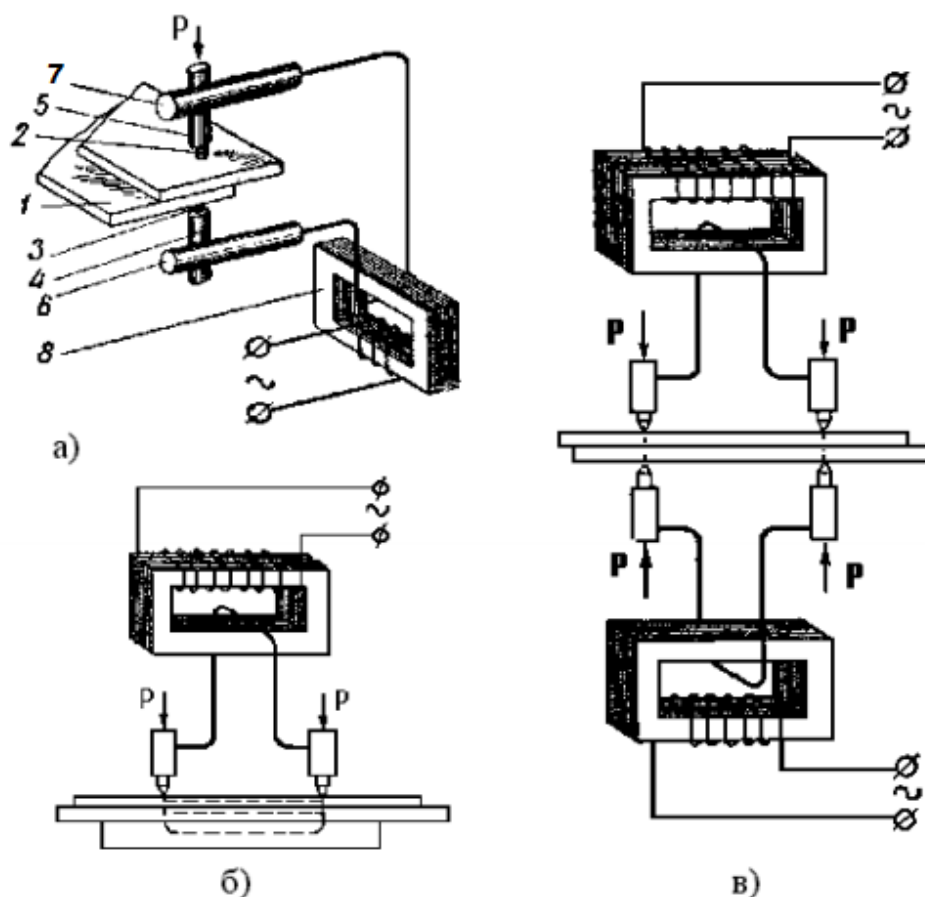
Схемы точечной контактной сварки:
